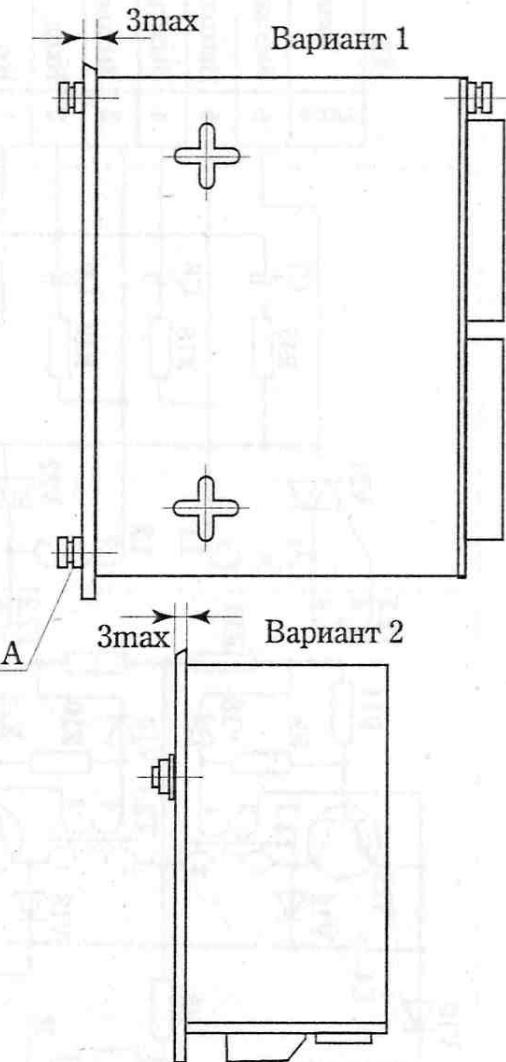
Габаритные и установочные размеры ПБР – 2М, ПБР – 2М1
